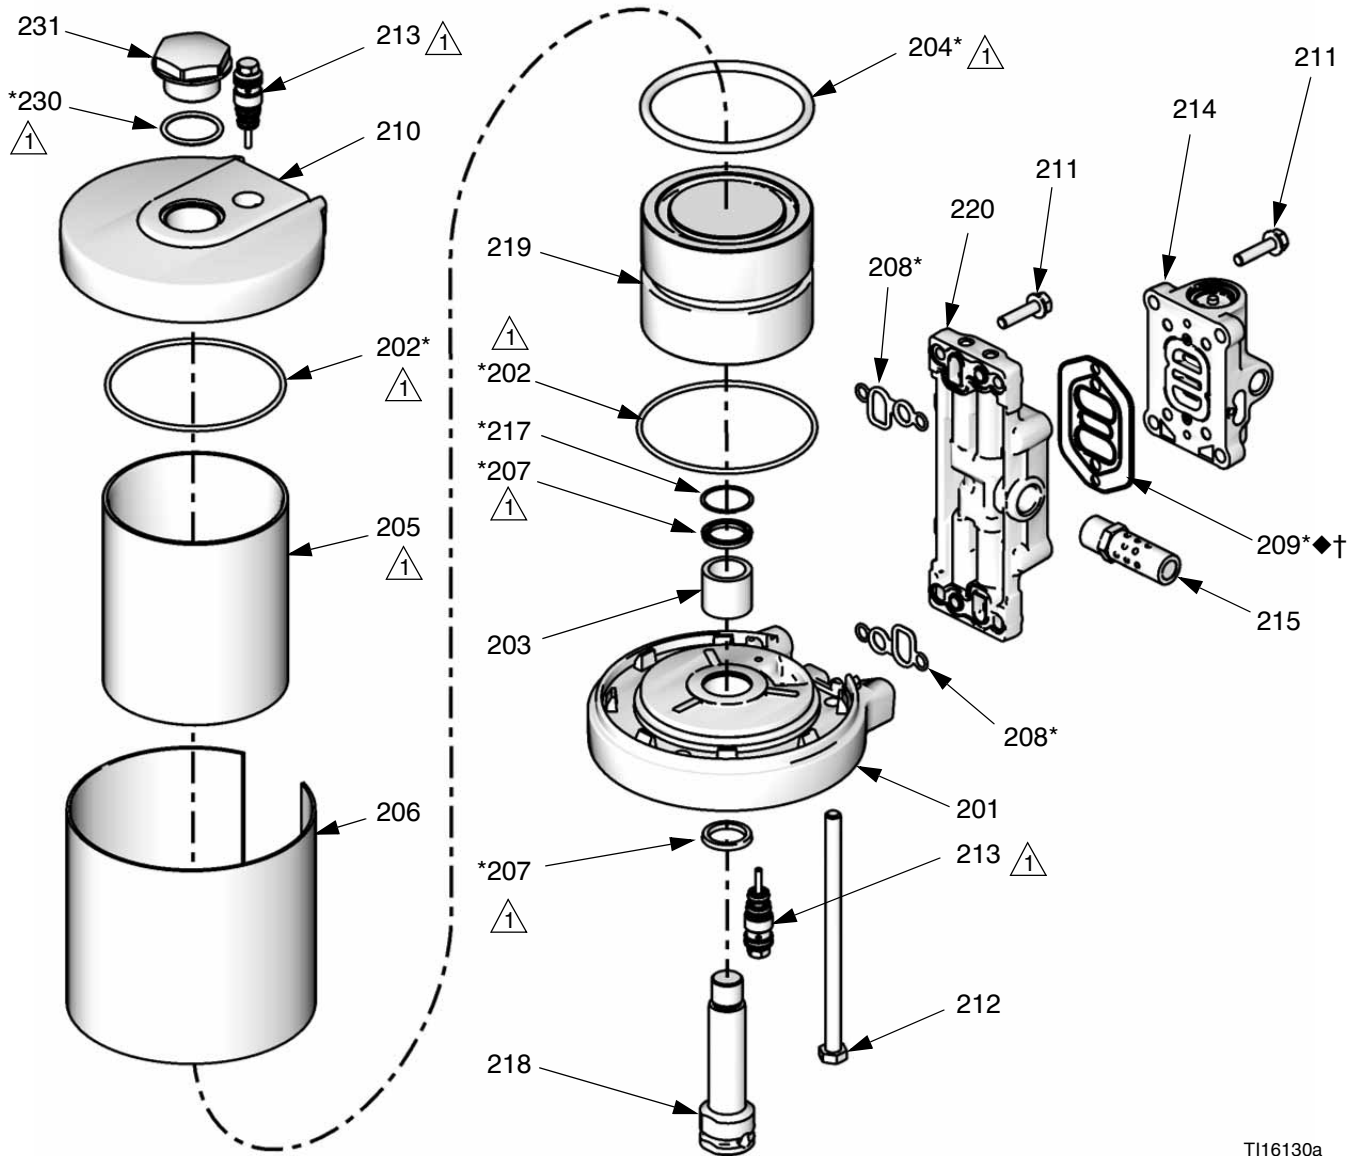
Установка П-образных уплотнительных колец пневмодвигателя
